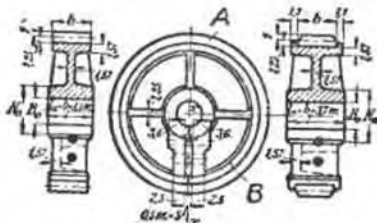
, 503 и 504 дают размеры нормальных цилиндрических колес фирмы Отто Грузон и К^о, Магдебург—Букау. Колеса бывают без или с боковыми дисками, цельными или свертными (на фиг. 501 наверху изображено цельное, внизу—свертное колесо). Для определения размеров в мм требуется помножить ука-
